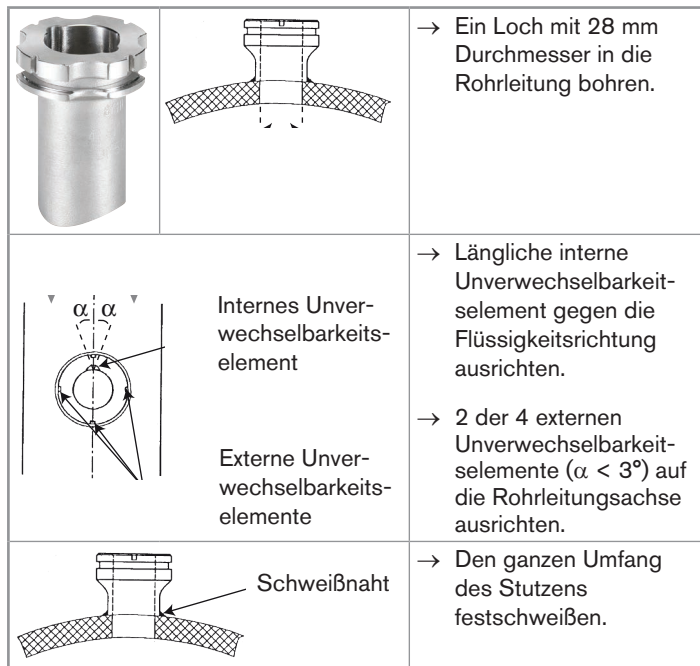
Installation eines Edelstahl-Schweißstutzens mit Radius
